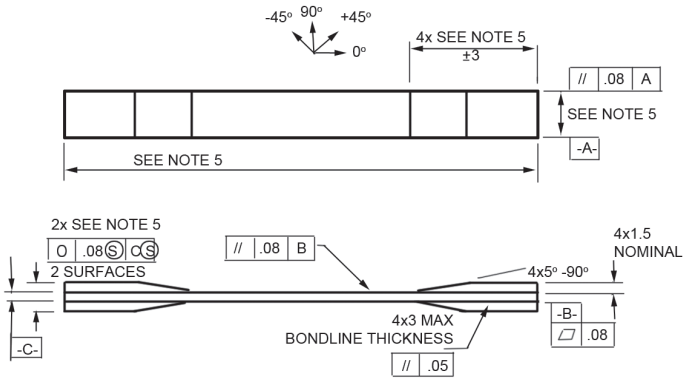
Прямоугольный плоский образец по стандарту ASTM D3039/D3039M-14 [5]
